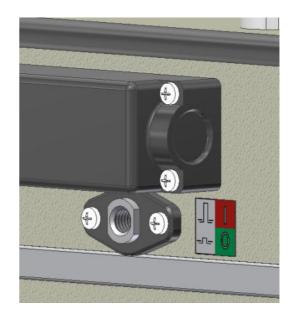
Присоединительные размеры блокировочных тяг и синхронизирующего вала ISM25_LD_1
